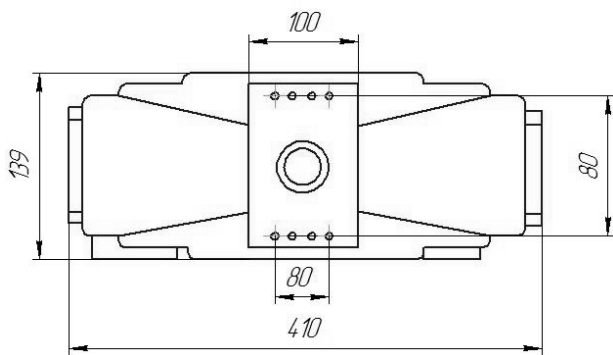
Вимірювальний пристрій автоматичного рефрактометра RFR: 1 – оптичний блок із закріплювальним фланцем; 2 – литий корпус
